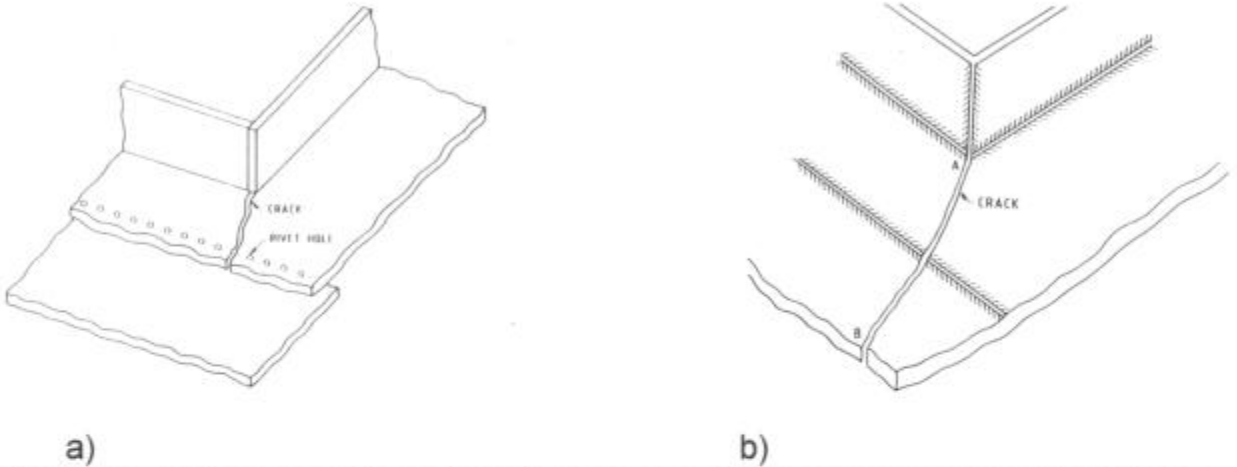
Propagación de fracturas en a) uniones remachadas y b) soldadas.
